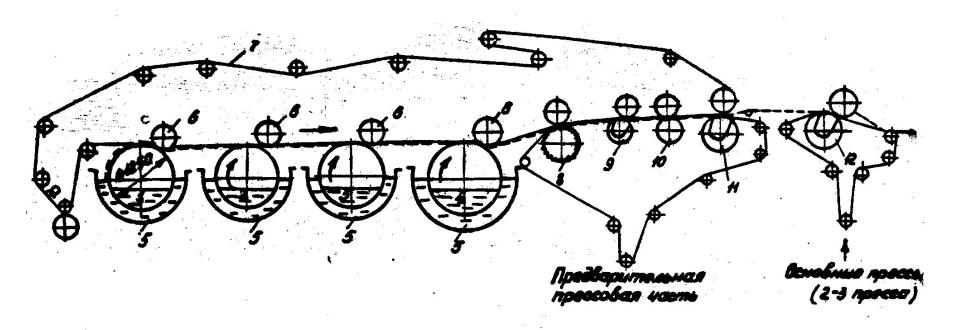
Схема круглосеточной бумагоделательной машини (с прямым ходом сукна); 1-2-3-4 — сеточные пилиндри; 5 — ванни; 6 — съемные валики; 7 — сукно; 8 — экстракторный пресс; 9 — отсасывающий пресс; 10 — обычный пресс; II — отсасывающий гаучвал; I2 — основной первый пресс.
